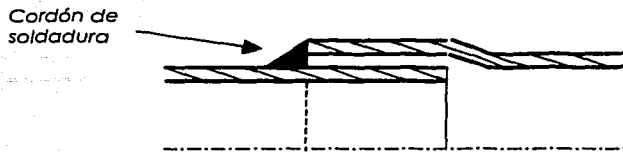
Ejemplo de unión por enchufe con cordón de soldadura.
